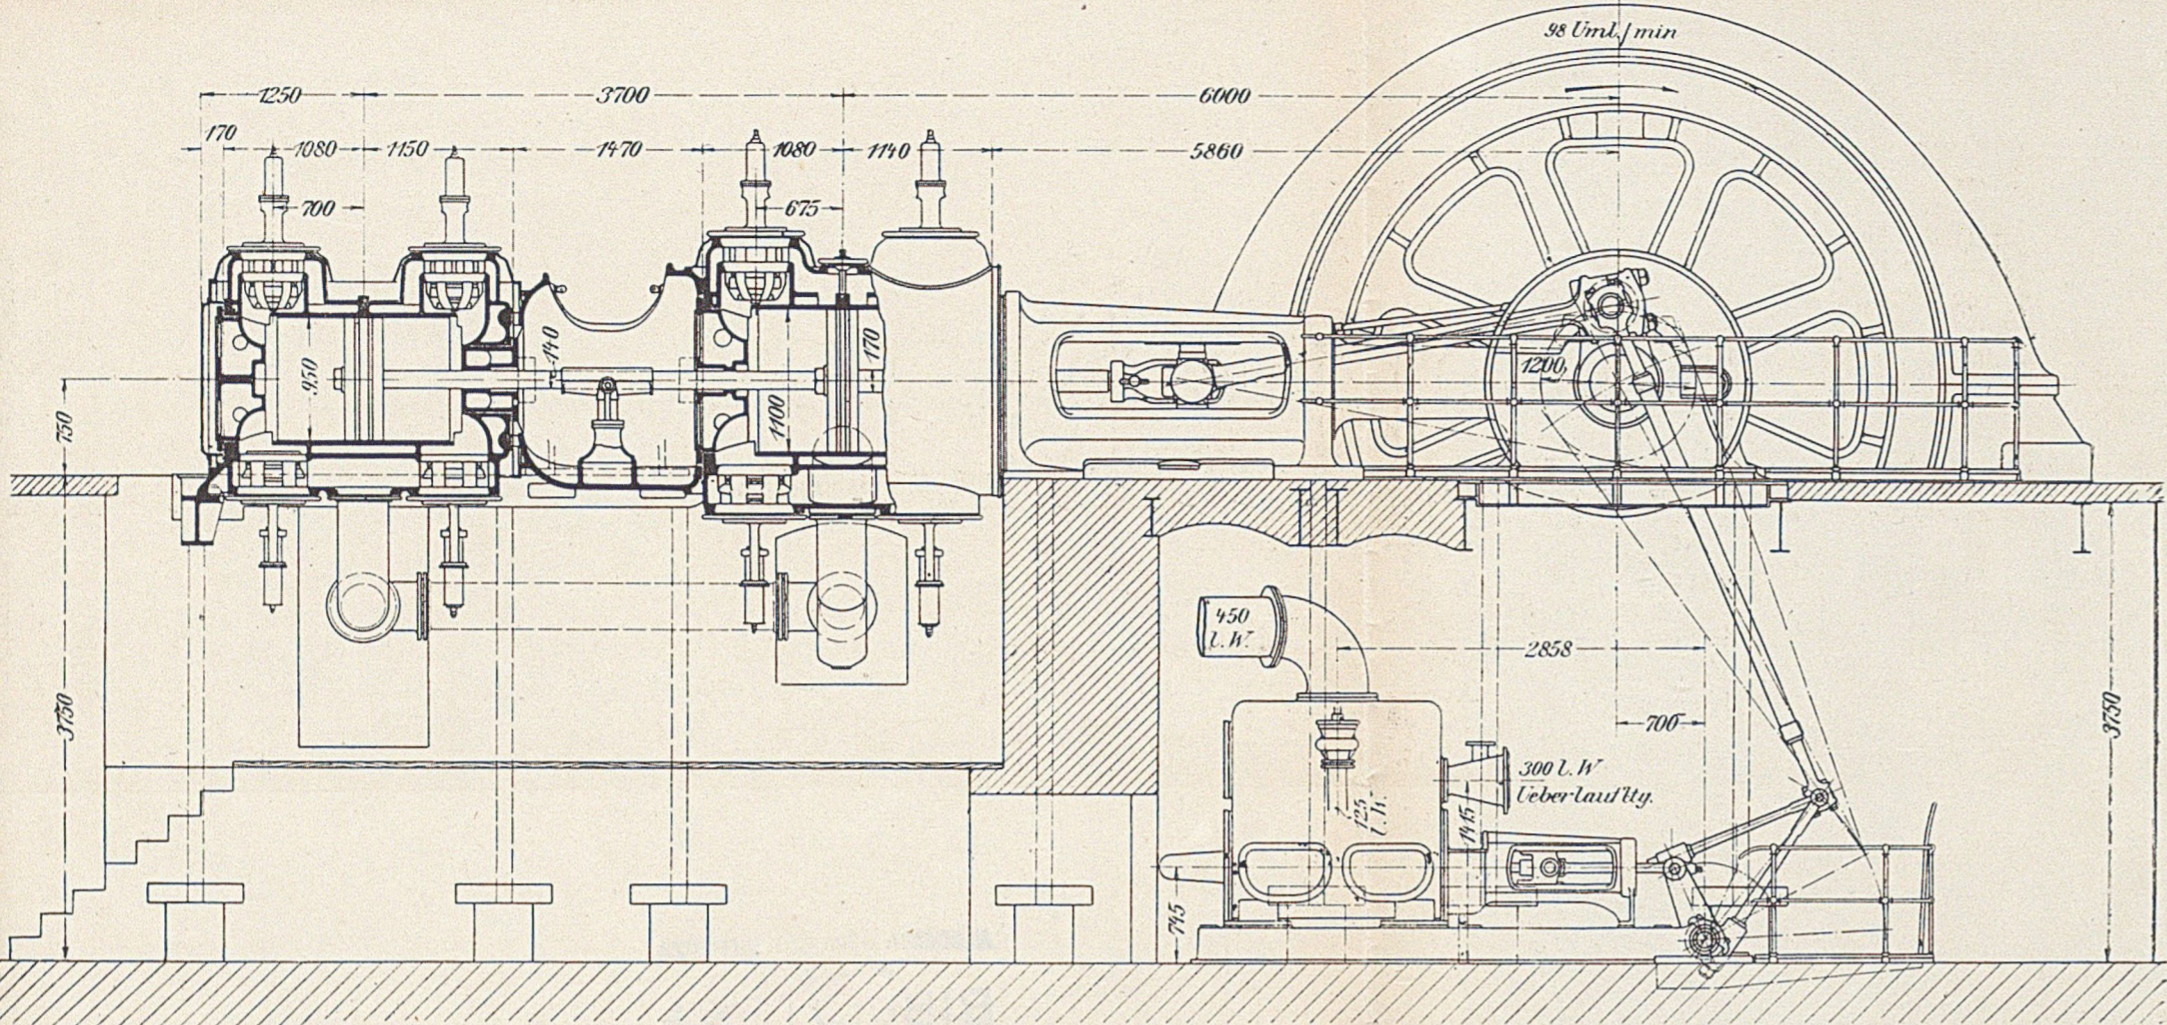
Aufriß und Schnitt durch die Zylinder.
